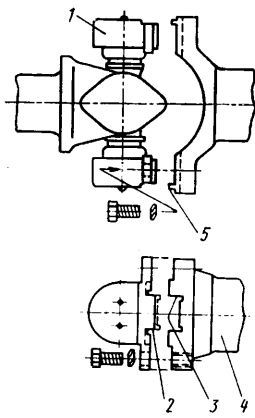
Карданный шарнир с безболтовым креплением игольчатых подшипников
